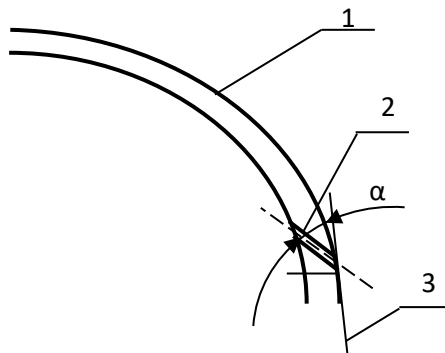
Профіль лопатки: 1- поверхня лопатки; 2 – повздожня щілина; 3 - дотична
